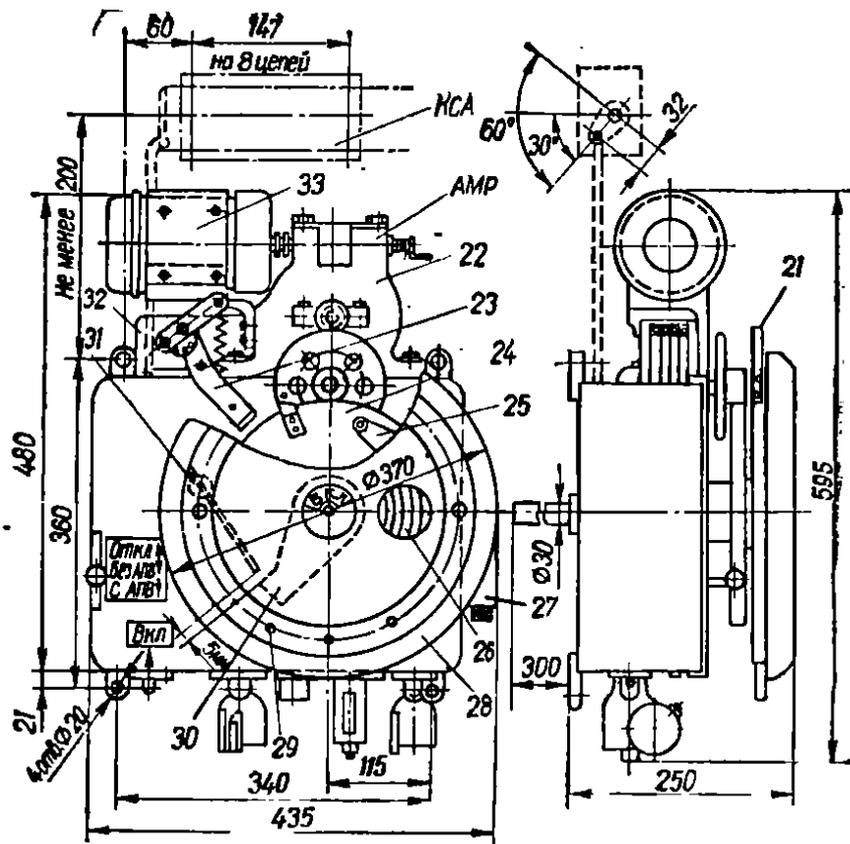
Общий вид пружинного привода типа ППМ-10
